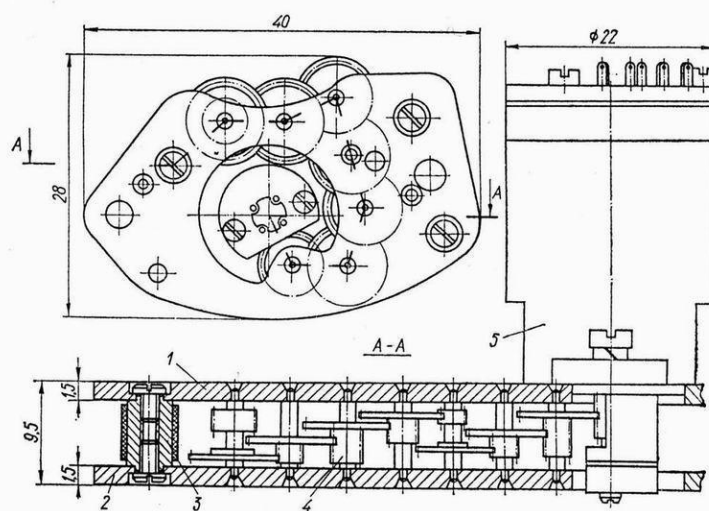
Конструкція двоплатного приладного редуктора
